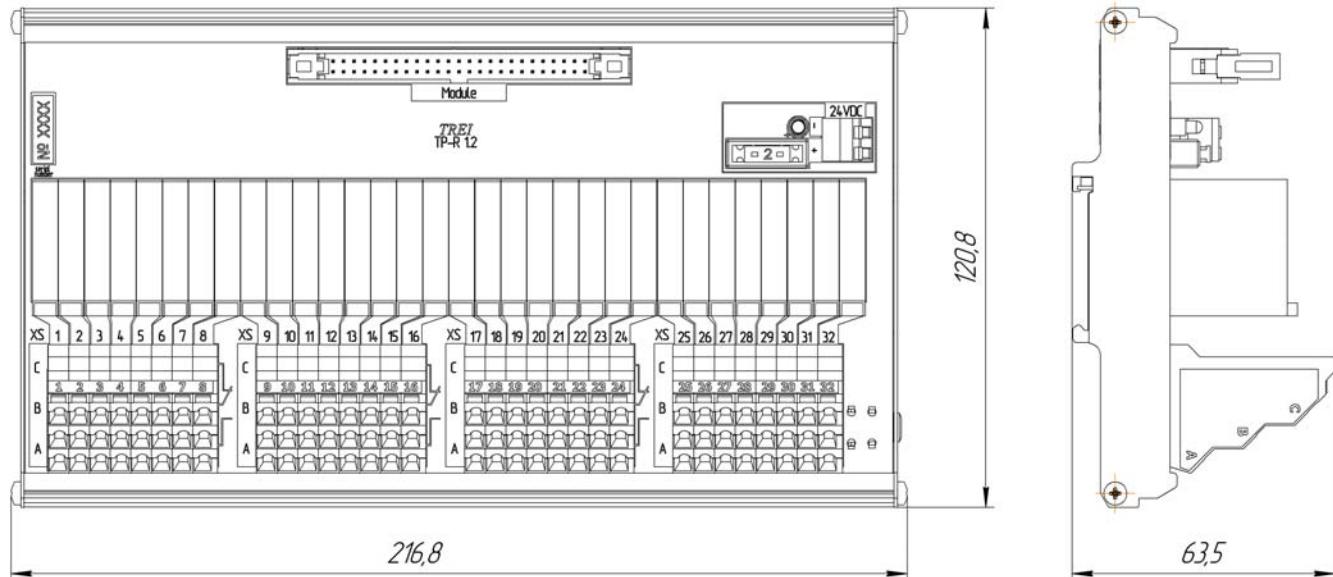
Чертеж общего вида TP-R (TP-R1, TP-R2) с указанием габаритных размеров
